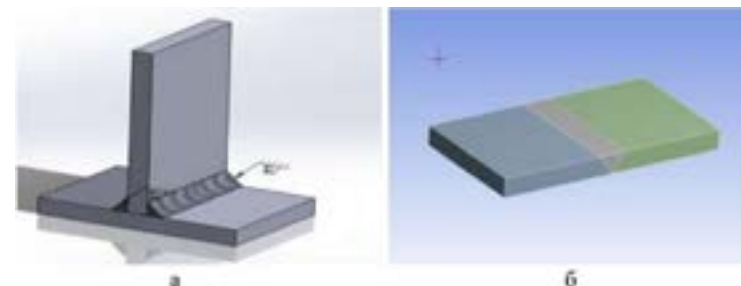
Сварное соединение: а) Т-образное соединение; б) сварное стыковое соединение
